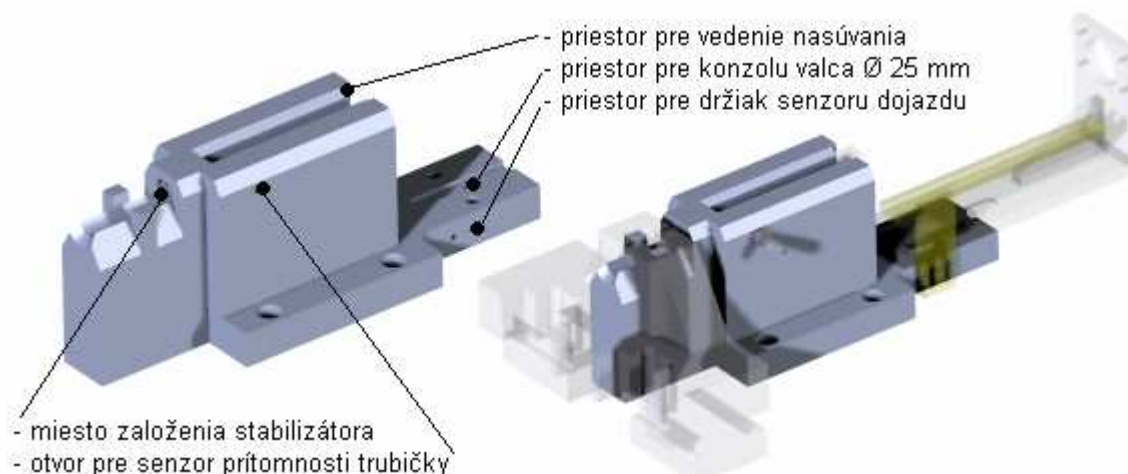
Základné teleso zariadenia, siluety aplikovaných komponent.
